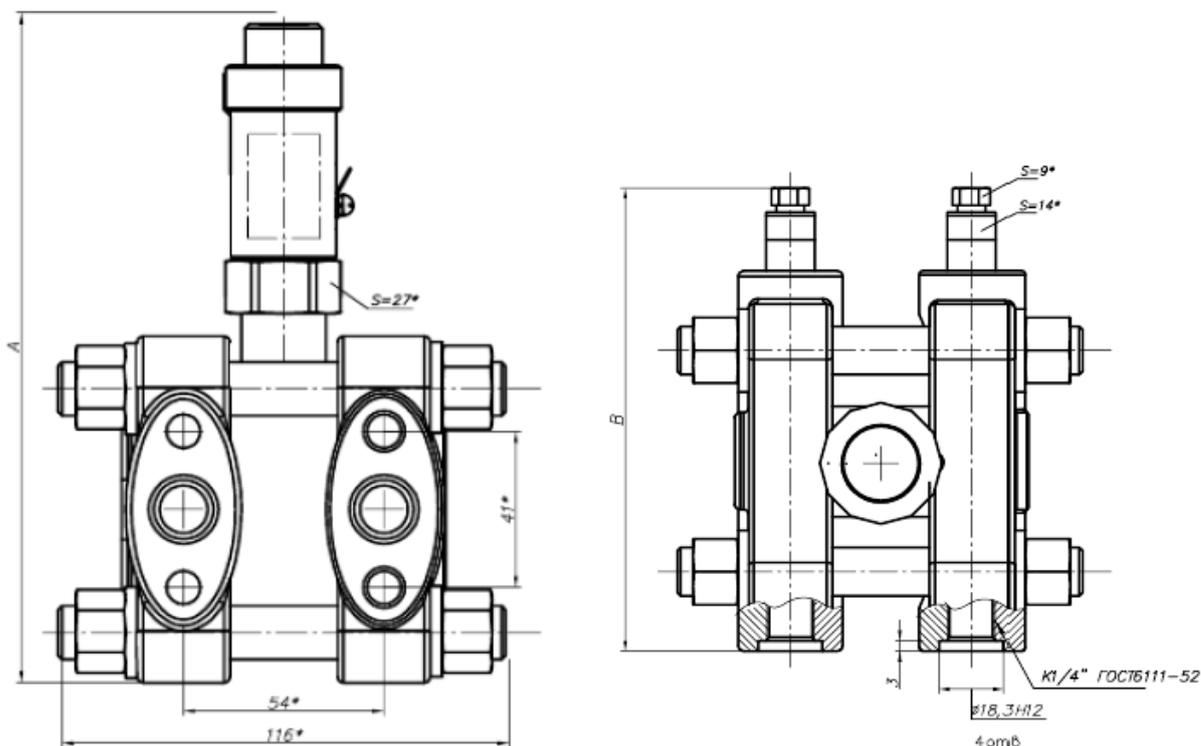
Габаритный чертеж преобразователей избыточного давления, разрежения, давления-разрежения с кодом присоединительного размера 9 и кодом конструктивного исполнения К14
